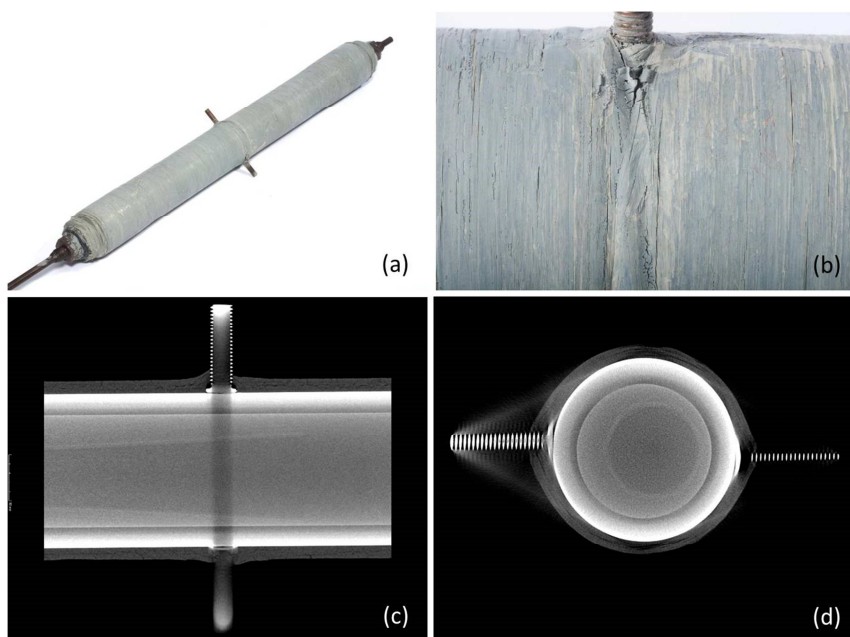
(a) Liner 7 mit zwei aufgeschweißten Bolzen und von SKT aufgebrachter UD-Wicklung; (b) gewickelte Nextel-Faser in der Nähe des Bolzens; (c) CT-Aufnahme des gewickelten Liners im Längsschnitt; (d) CT-Aufnahme im Querschnitt
